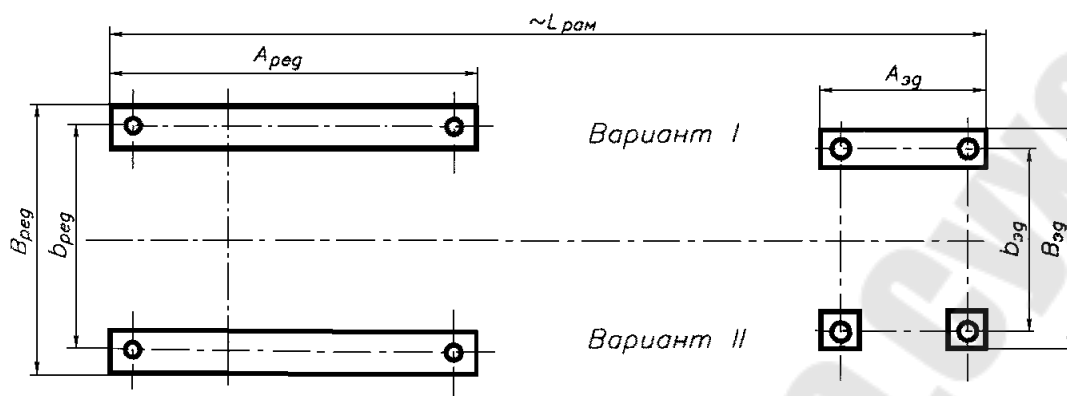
Размещение опорных поверхностей электродвигателя и редуктора на раме
